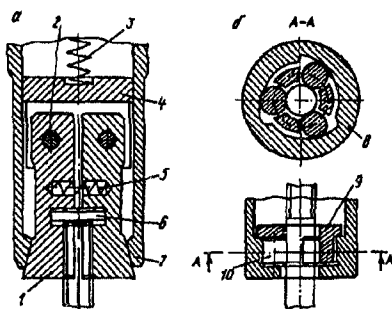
Патроны приспособлений для закрепления и заворачивания шпилек
